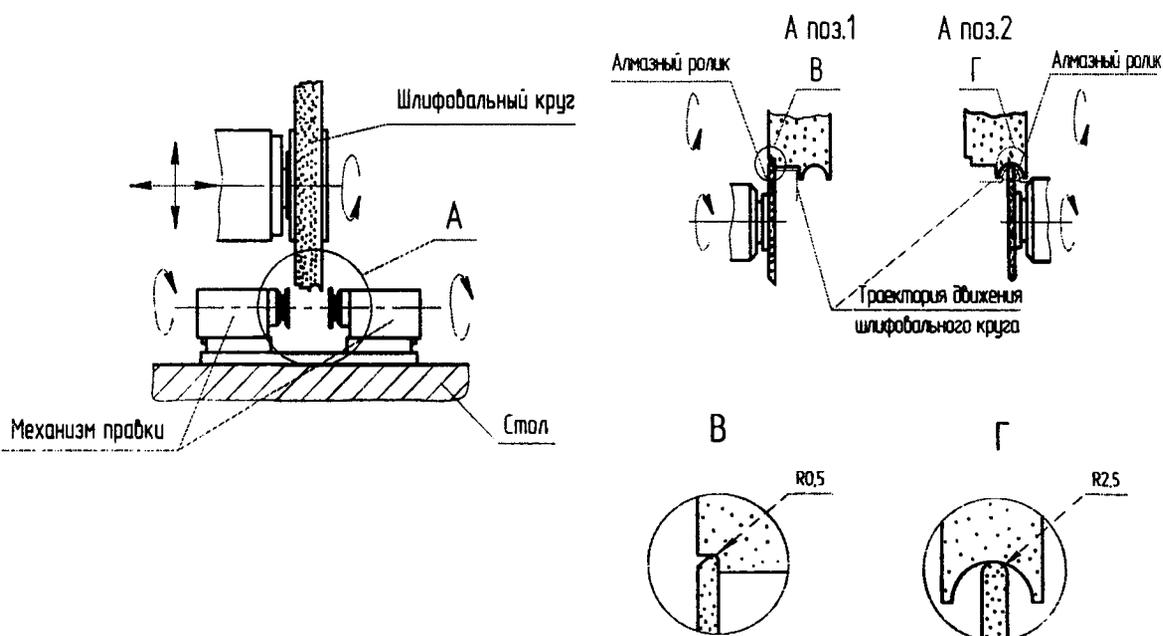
Правка шлифовального круга двумя алмазными роликами
